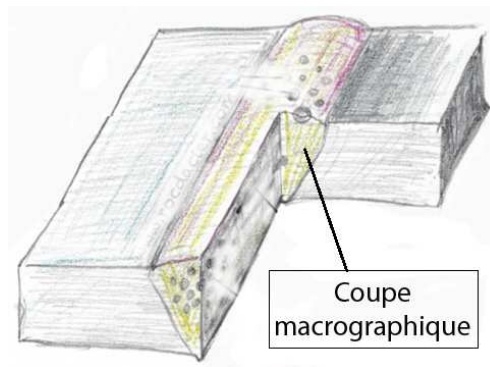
Définition de la macrographie du cordon de soudage ©Rocdacier [118].
